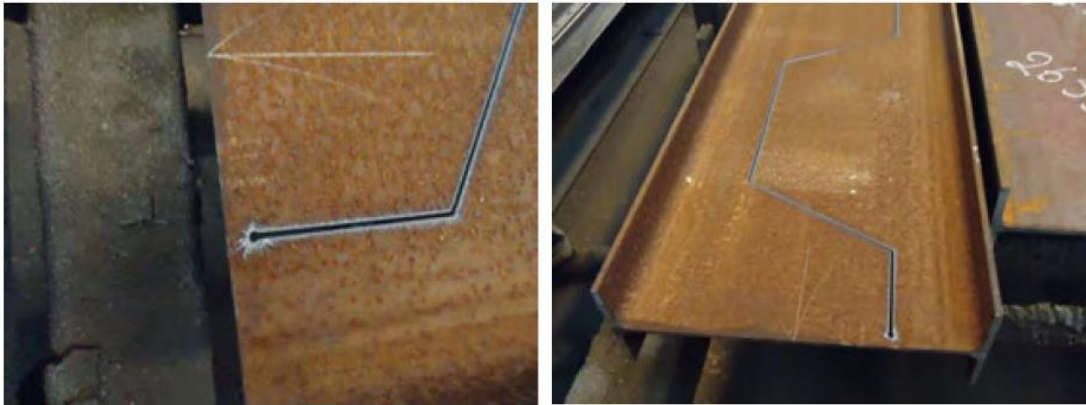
Processo de soldagem na fabricação das vigas casteladas
